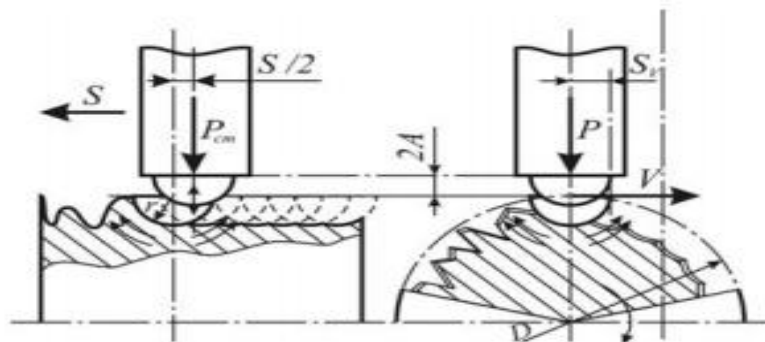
Схема поверхностного пластического деформирования при ультразвуковой упрочняющей обработке
